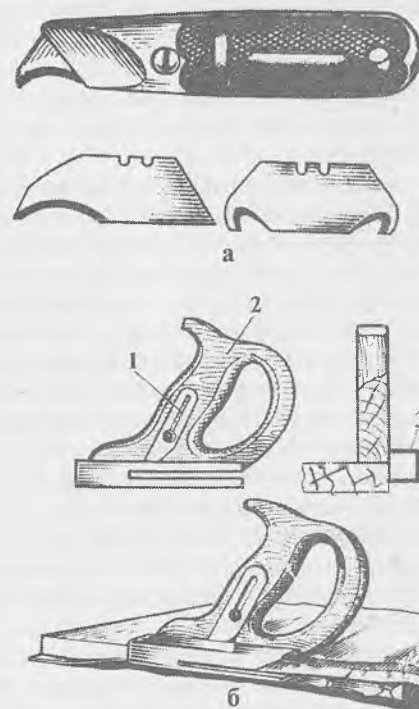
Резцы (а) и приспособление (б) для снятия свесов шпона в заготовках после их облицовывания:
